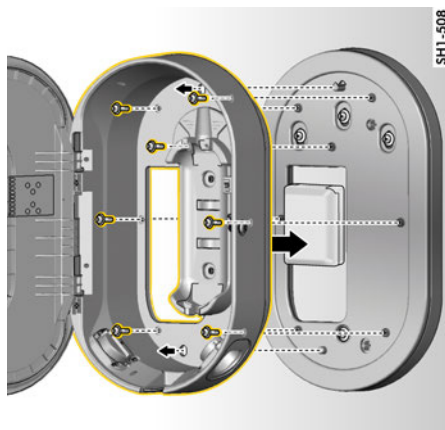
Atornillado del puerto de carga en la placa de montaje
